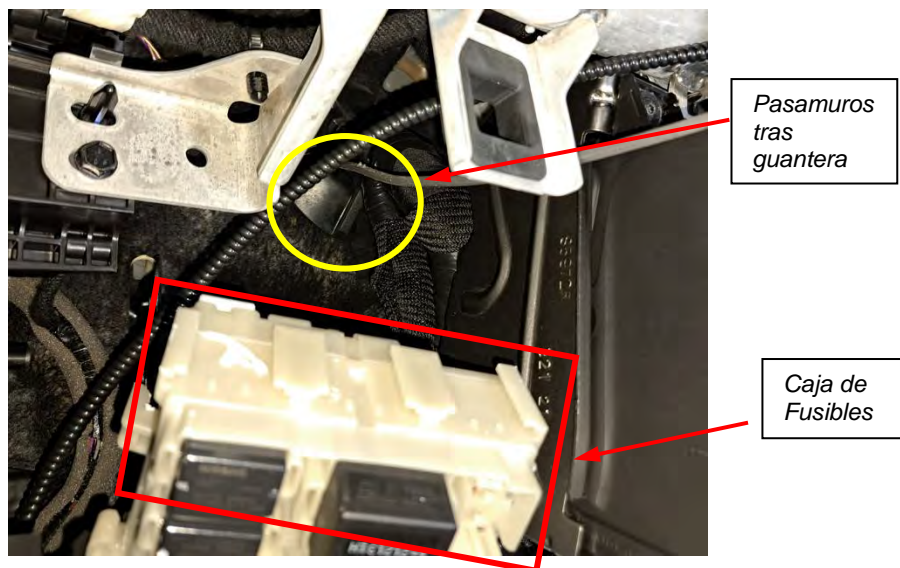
Ubicación y detalle de pasamuros tras la guantera del pasajero desde el habitáculo interior.
